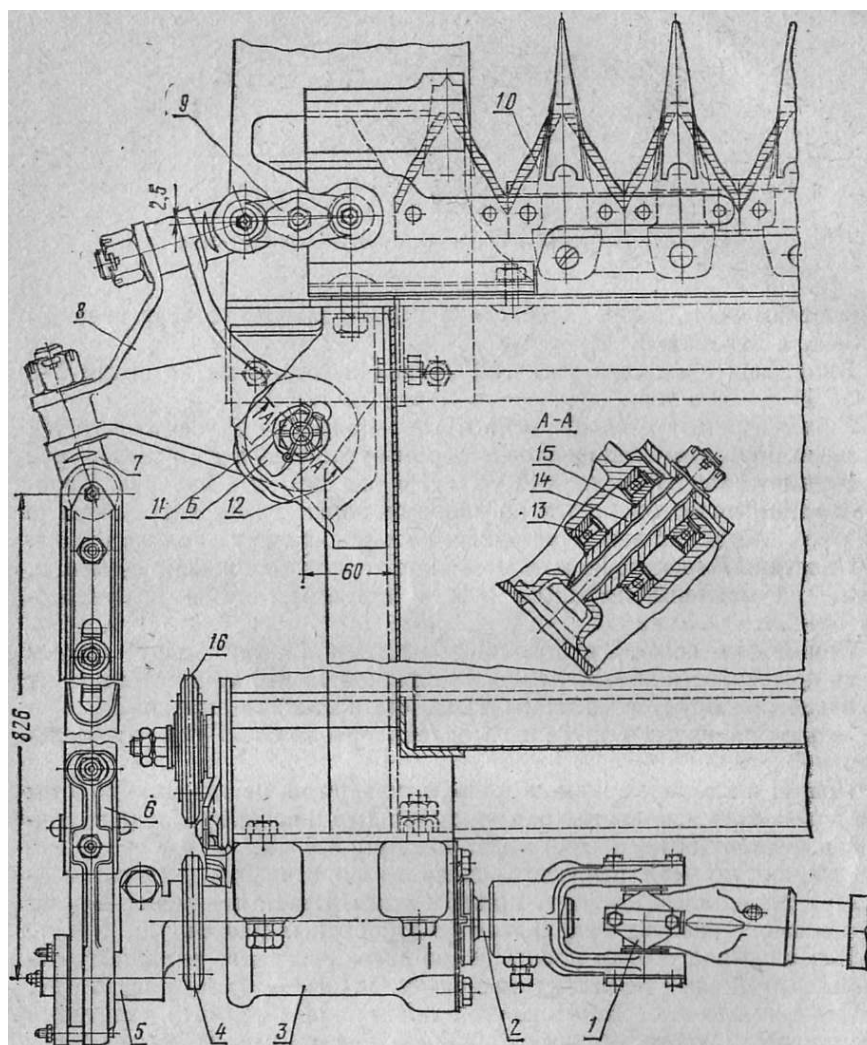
Кривошипно-шатунный механизм привода ножа:
